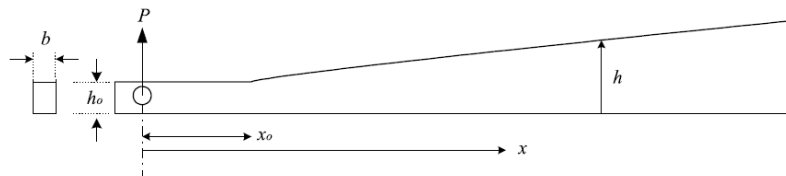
Talon TDCB [8] – Vue de face et vue de côté
